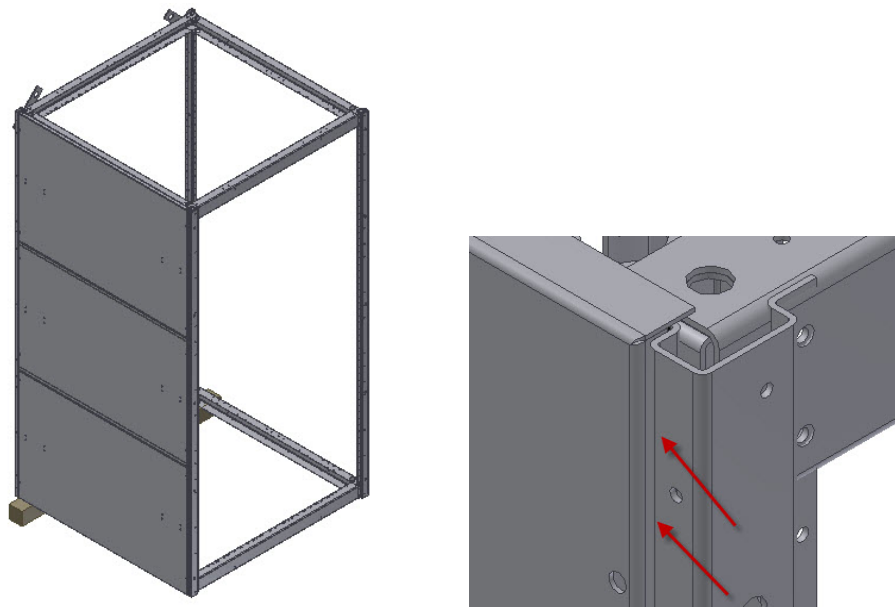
Ensamble de cubiertas posteriores contra la estructura base.
